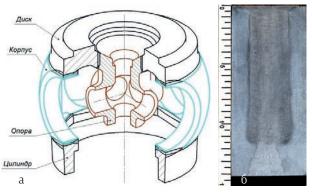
Эскиз сварного корпуса рабочего колеса (a) и макроструктура сварного шва (б)
